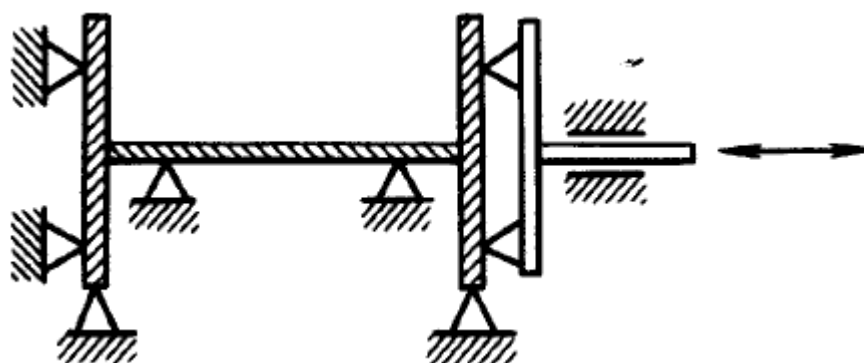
Схема кондуктора для сборки двутавровых балок
